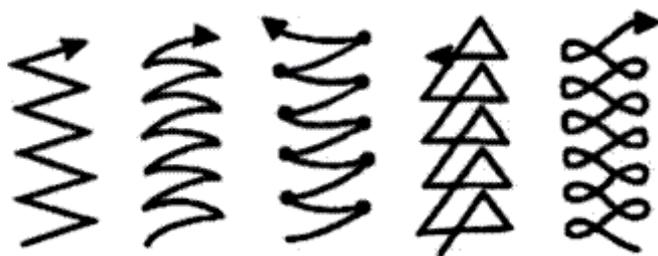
Основные траектории движения конца электрода при ручной дуговой сварке широких швов
